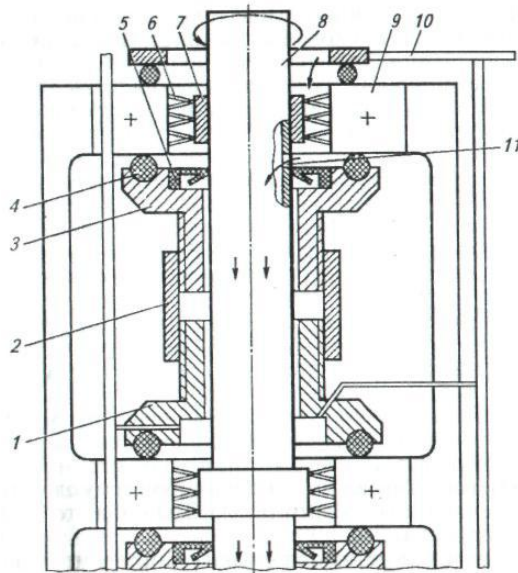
Схема анодного пристрою для відновлення опор під підшипники електроконтактним способом; 1 і 3 – втулки підшипника; 2 – гайки; 4 – кільце, ущільнювача; 5 – сальник; 6 – тампон; 7 – анод; 8 – полий вал; 9 – блок циліндрів; 10 – гумова трубка; 11 – електроліт.
